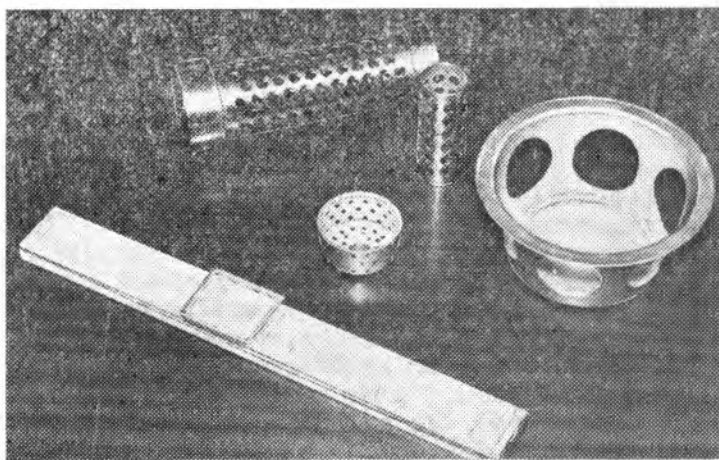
Детали, отверстия в которых пробиты полиуретаном за один ход пресса
